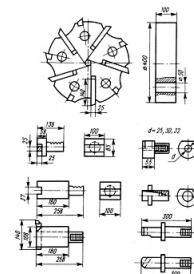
Типовые резцовые блоки крепления цилиндрическим хвостовиком с реечным зацеплением
